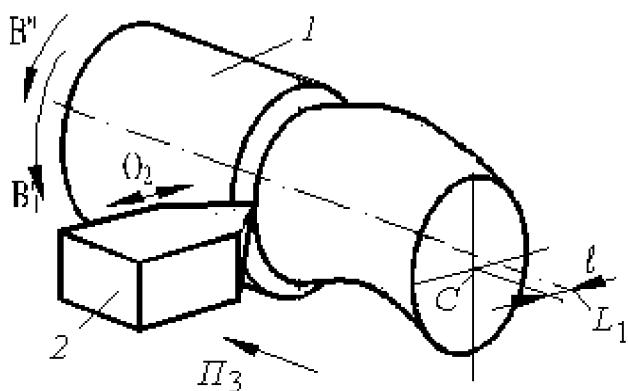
Кинематическая схема обработки круговой винтовой поверхности
